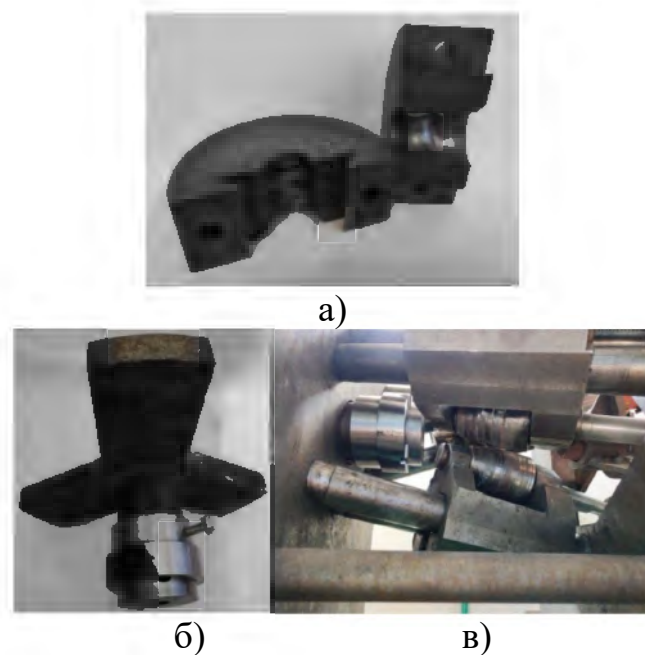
Экспериментальная установка для формирования винтового арматурного профиля: а - винтовая матрица, б – крепление винтовой матрицы в обойме, в – общий вид деформирующего узла
